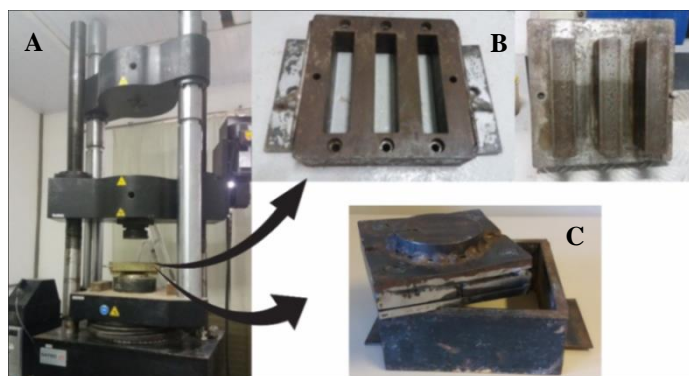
Máquina de ensaios universais Instron (A), moldes macho e fêmea retangular (B) e molde usado para a produção de amostras quadradas (C).
